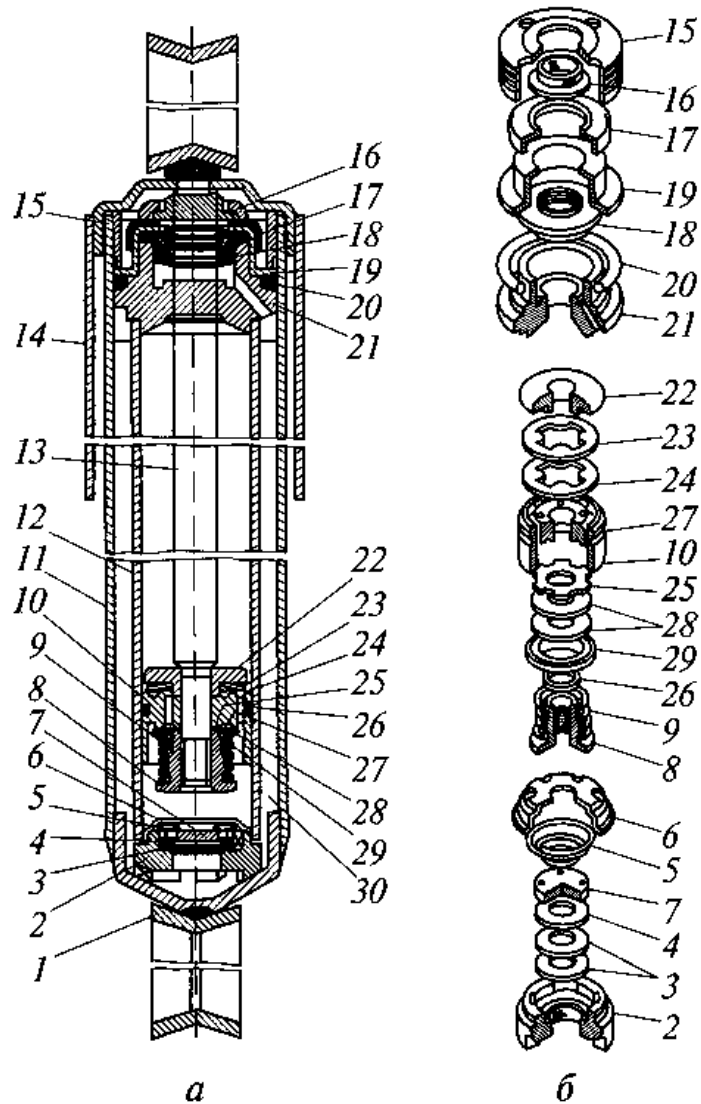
Амортизатор: а – загальний вигляд; б - деталі амортизатора; 1 - провушина; 2 - днище; 3, 4, 25, 28 - диски; 5, 9, 23 - пружини; 6, 19 - обойми; 7, 22 - тарілки; 8, 15 - гайки; 10 - поршень; 11 - резервуар; 12 - циліндр; 13 - шток; 14 - кожух; 16, 27 - кільця; 17, 20 - ущільнювачі; 18 - манжета; 21 - втулка; 24, 29 - клапани; 26 - шайба; 30 - камера
